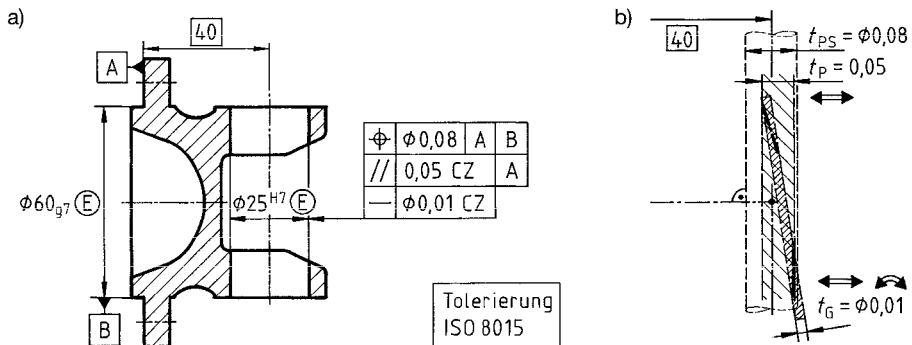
Flanschstück einer Gelenkwelle. a) Zeichnungsausschnitt (vereinfacht) mit Toleranzangaben, b) Veranschaulichung der drei Toleranzzonen dazu
